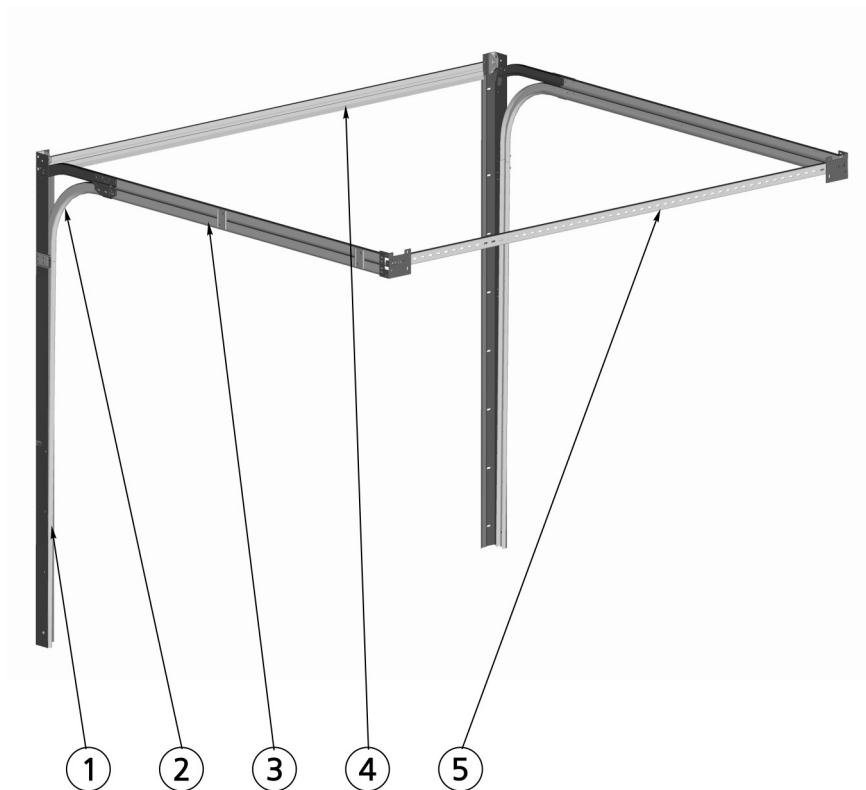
Схема несущего каркаса ворот. Низкий монтаж
